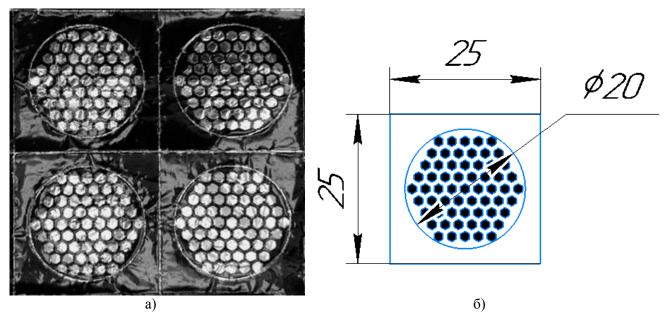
a) внешний вид полученного образца; б) чертёж фотошаблона
